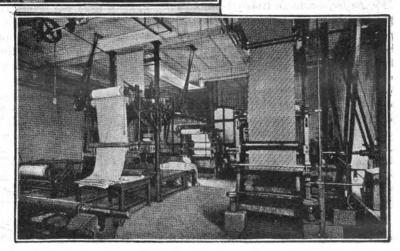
MACHINES A IMPRIMER DES LABORATOIRES DE TEINTURE.
